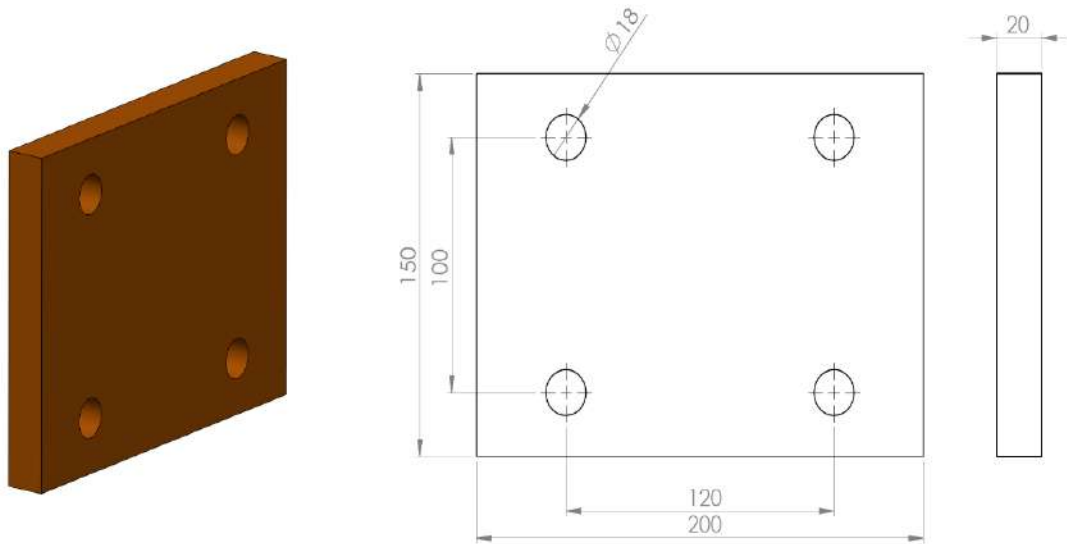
a) Modelo 3D de la brida plana empleada en la unión. b) Planos acotados de alzado y perfil de la brida plana empleada en el modelo de simulación y en el ensayo de laboratorio.
